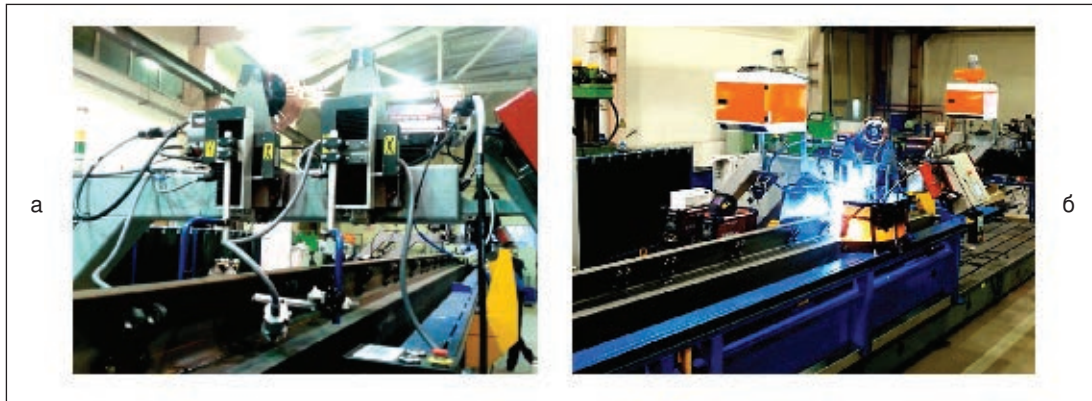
Общий вид установки для автоматической сварки хребтовой балки с дугавром: а — в процессе наладки; б — в процессе сварки
